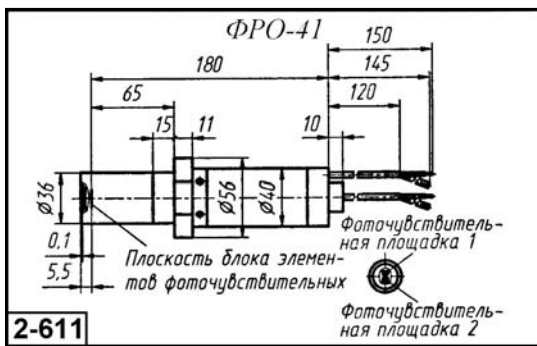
Внешний вид и габаритные размеры фоторезистора ФРО-41
